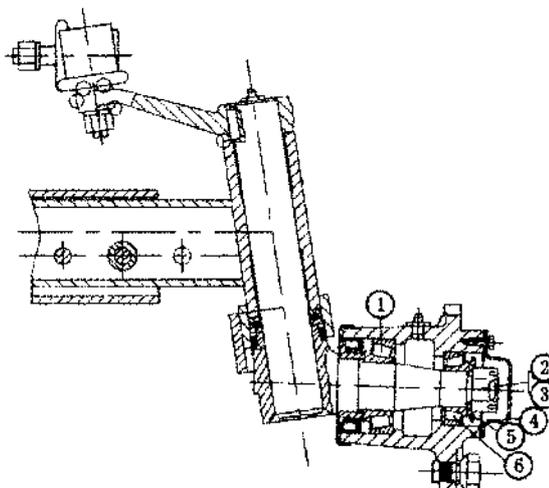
10. Регулировка зазора по оси подшипника передних колес
